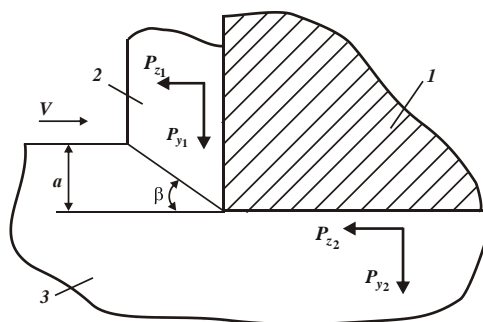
Расчетная схема параметров процесса точения с учетом трения на задней поверхности резца: 1 – резец; 2 – образующая стружка; 3 – обрабатываемый материал ( $\beta$  – условный угол сдвига обрабатываемого материала)
